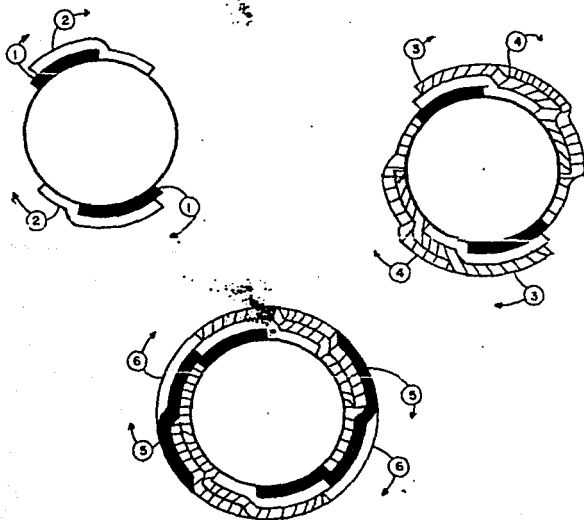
DETALLES DE SOLDADURA EN LA INSTALACION DE ACCESORIOS Y SECUENCIA DE MONTAJE DE PUERTAS
